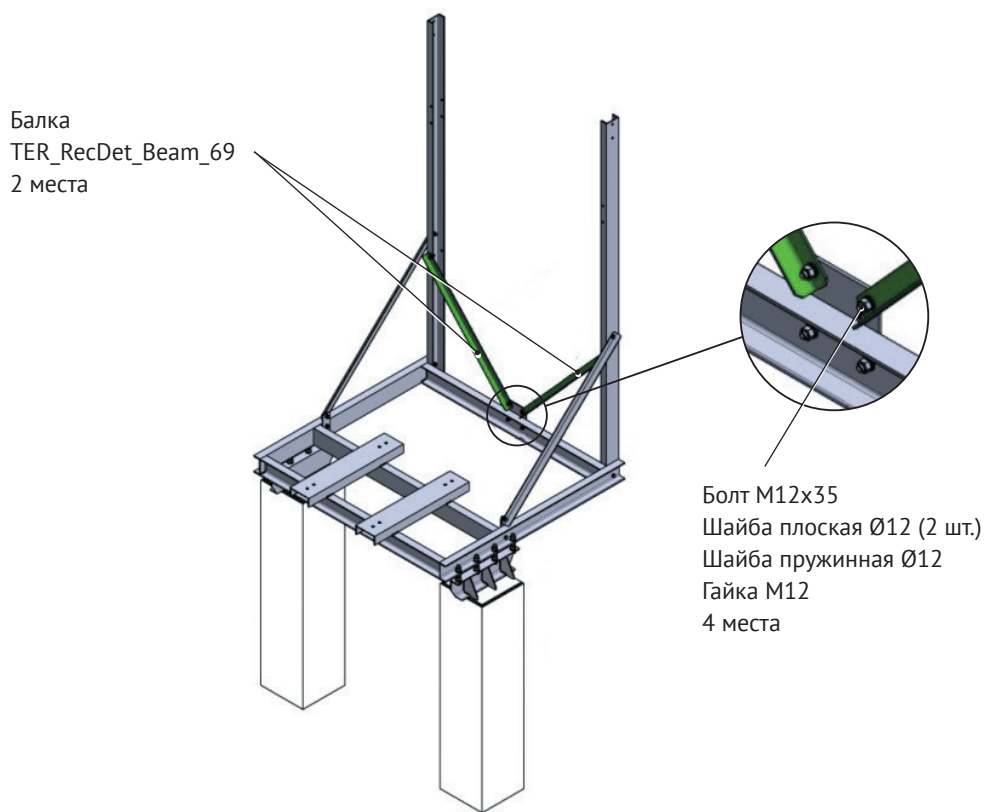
Крепление балок поперечных к стойкам предохранителей
